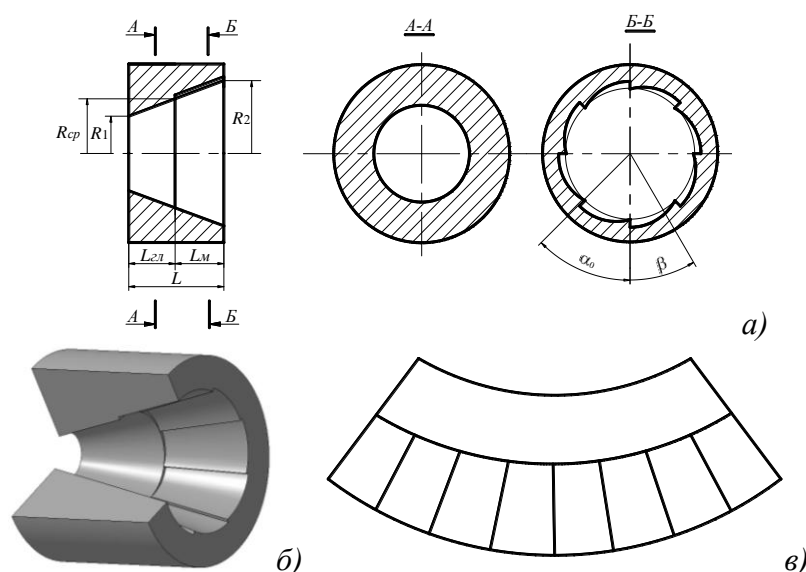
Конический гибридный гидродинамический подшипник: а) расчетная схема; б) 3D-модель; в) развертка опорной поверхности
